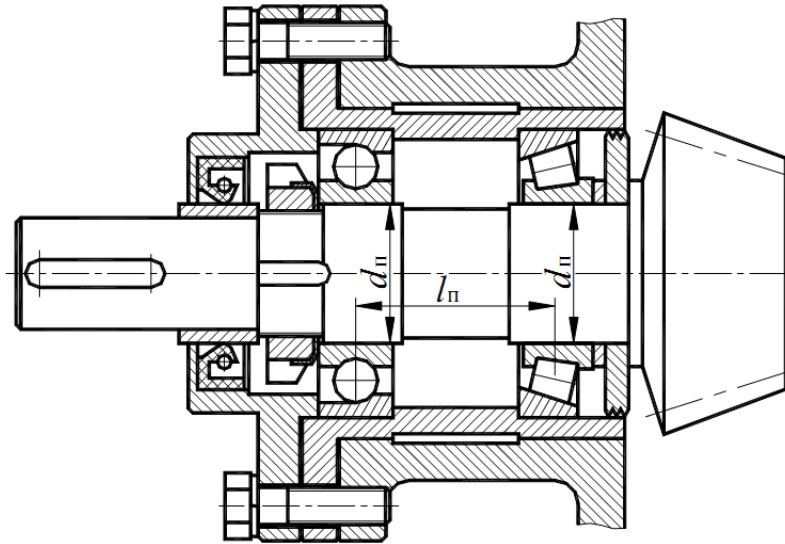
Установка вала на радиально-упорных подшипниках "вращающую"
